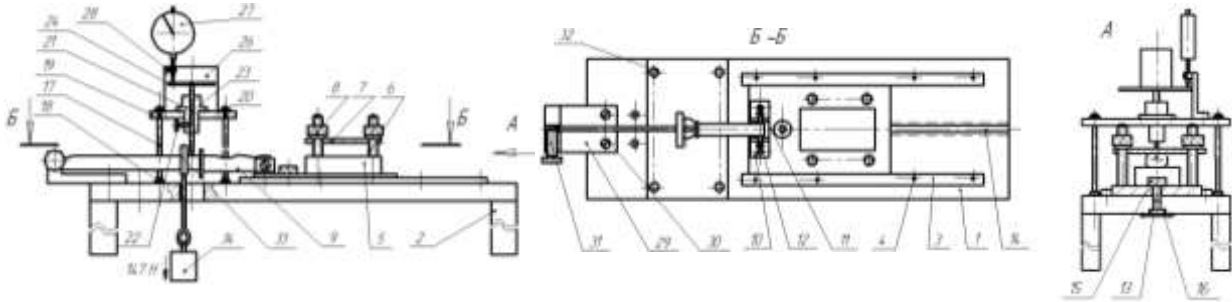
Схема налагодження пристрою для визначення міцності конструкції вузла фіксатора клинка: 1 – корпус; 2 – ніжки; 3 – напрямні; 4 – гвинти; 5 – рухомий столик; 6 – шпильки; 7 – пластина; 8 – гайки; 9 – руків'я; 10 – опорний елемент; 11 – гвинт; 12 – гвинт регулюючий; 13 – болт стопорний; 14 – Т-подібний паз; 15 – гайка; 16 – пластина; 17 – стойка; 18 – гайка; 19 – пластина; 20 – гайка; 21 – напрямна; 22 – гвинт стопорний; 23 – вимірювальний штир; 24 – пластина; 26 – опора; 27 – вимірювальний прилад; 28 – гвинт; 29 – кронштейн; 30 – гвинт; 31 – гвинт; 32 – різьбові отвори; 33 – хомут; 34 – вага
